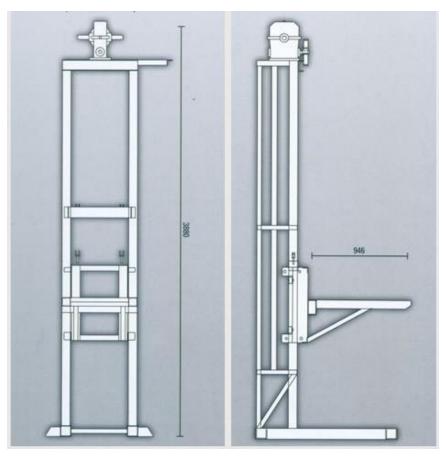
Vista Frontal y Lateral del Bajador de Jaulas Propuesto. Fuente: http://www.indumetavi.com.ar/es/equipos/equipo_para_bajar_jaulas.htm.
